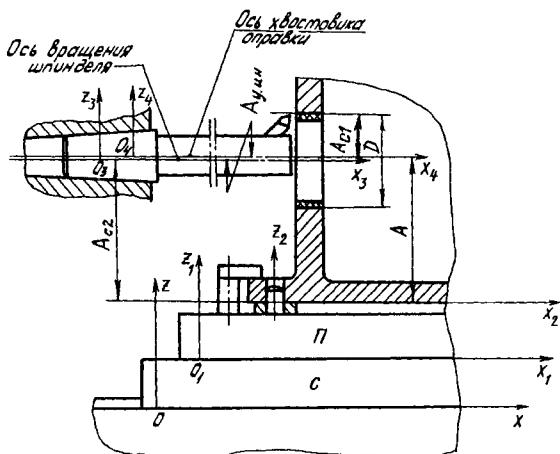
Задачи статической настройки горизонтально-расточного станка непосредственно через обработку заготовки
